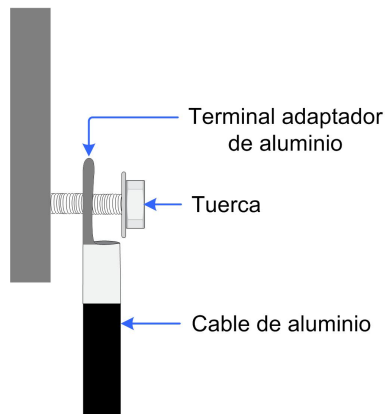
Secuencia de conexión de terminal del cable de aluminio
